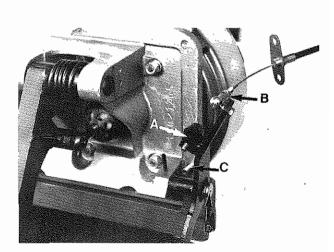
A - Tampone di fondo corsa Travel end pad
